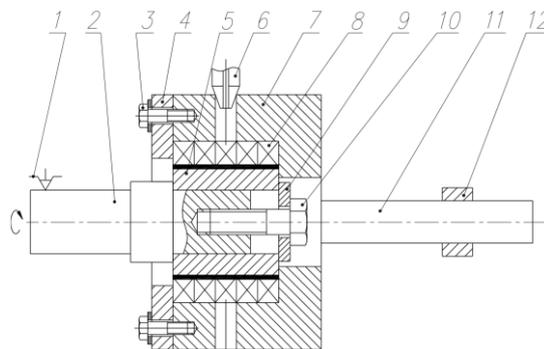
Схематичне зображення пристосування для проведення зносостійких випробувань: 1 – трикулачковий самоцентрувальний патрон; 2 – оправка; 3, 10 – кріпильні болти; 4 – фланцевий елемент; 5 – захисна втулка; 6 – система краплинної подачі; 7 – корпус пристосування; 8 – сальникова набивка; 9 – шайба; 11 – державка; 12 – різцетримач.
